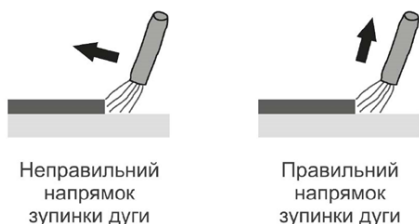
Напрямок зупинки дуги під час ручного дугового зварювання («ММА»).
